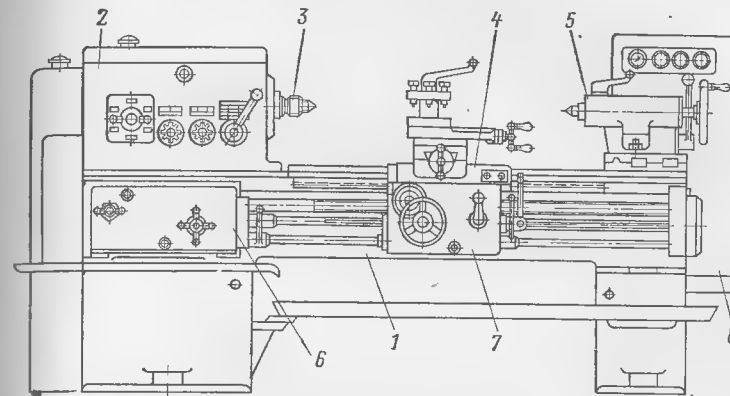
Общий вид токарно-винторезного станка модели 1K62Б.
